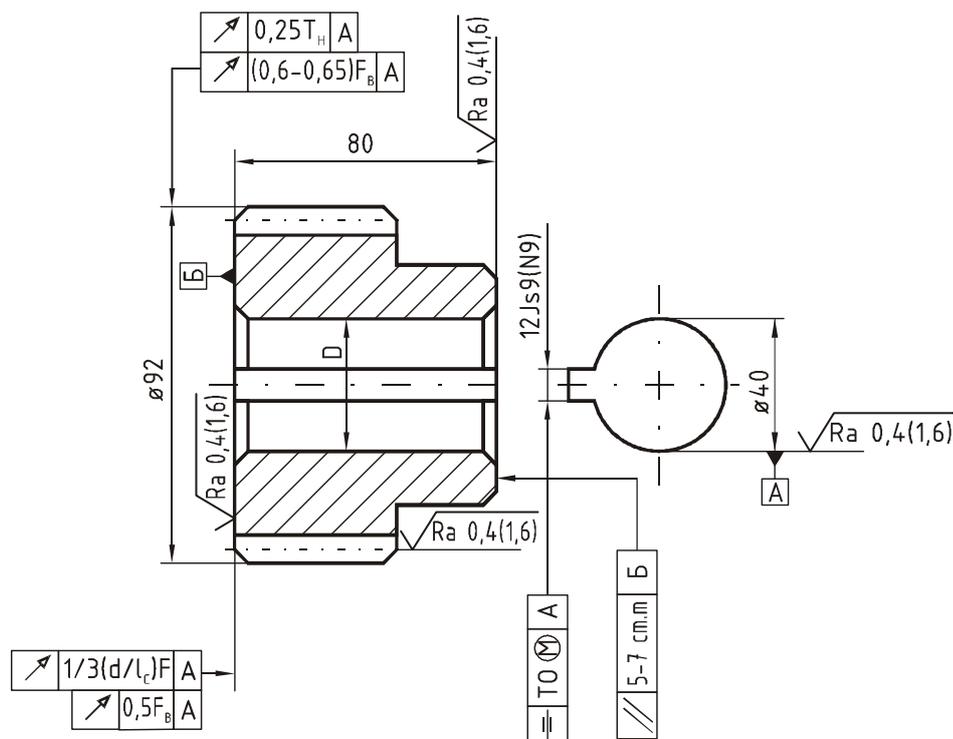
Зубчатое колесо с типовыми требованиями к точности его изготовления
